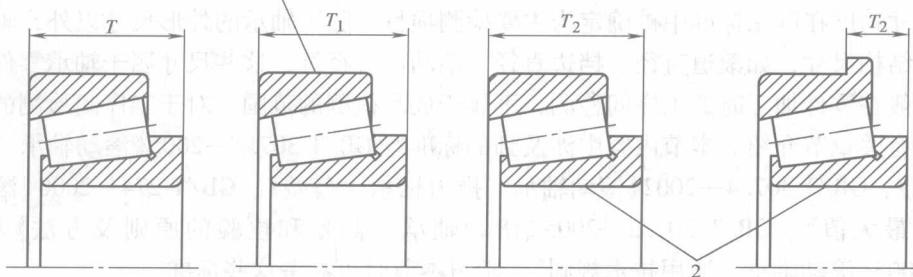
圆锥滚子轴承的公称宽度附加尺寸示意图
